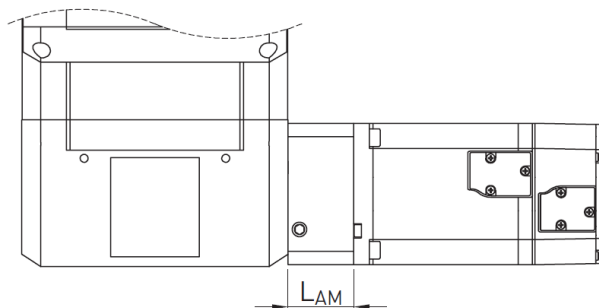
Motoraansluiting lineaire module HM-B zonder reductor
